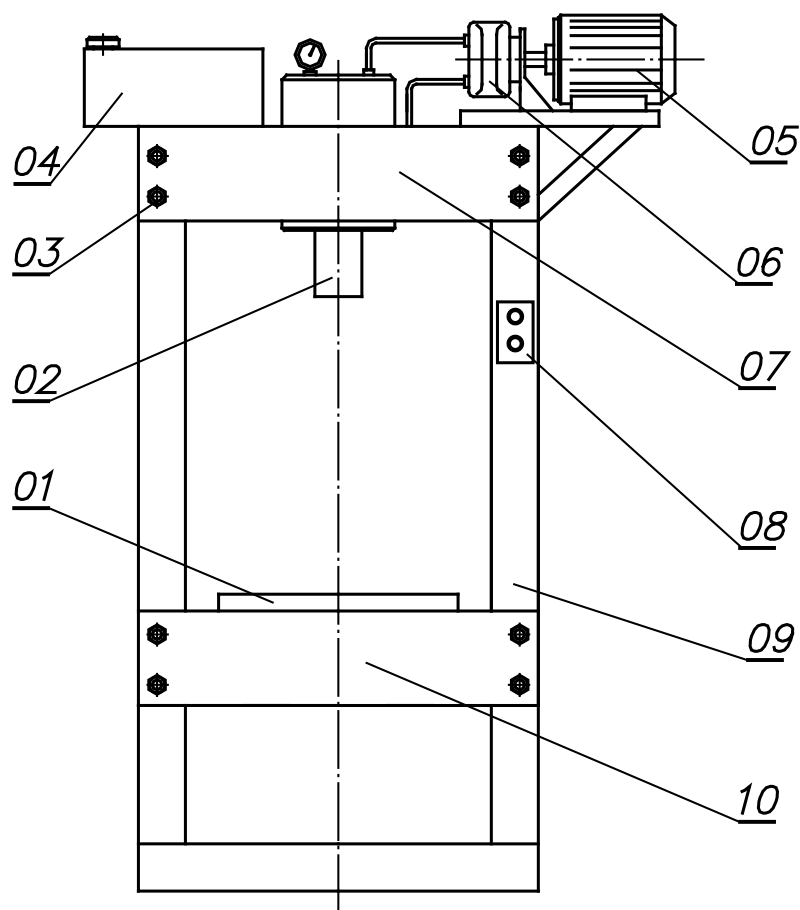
Гидравлический пресс. 01-стол; 02–гидроцилиндр ; 3-гайки;
